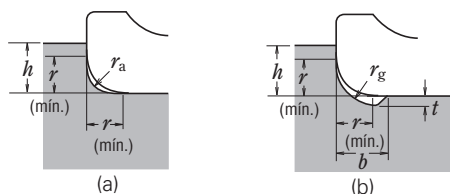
2 Dimensiones del Chaflán y Altura de Codo
